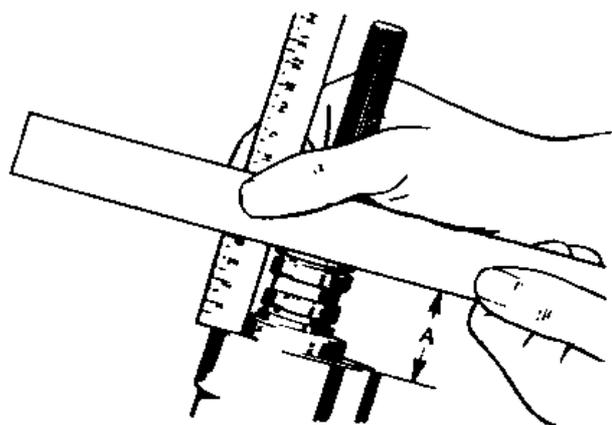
Предварительная регулировка подшипника шестерни (Разд.35)
